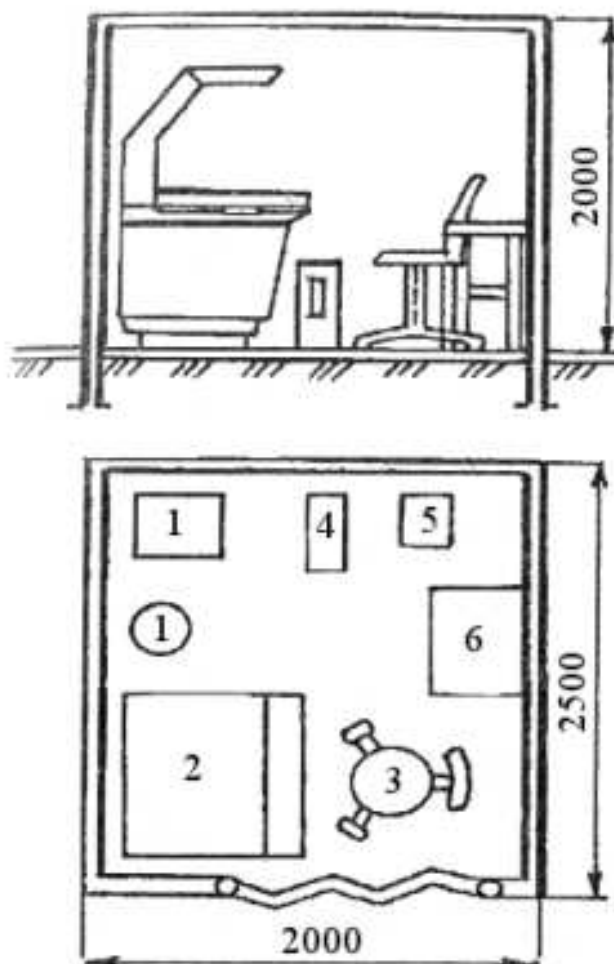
Сварочная кабина ООО «ПК ВентКомплекс»: 1 - источник тока; 2 - стол; 3 - стул; 4 - тумба; 5 - шкафчик; 6 - стеллаж; 7 - баллон с защитным газом.
